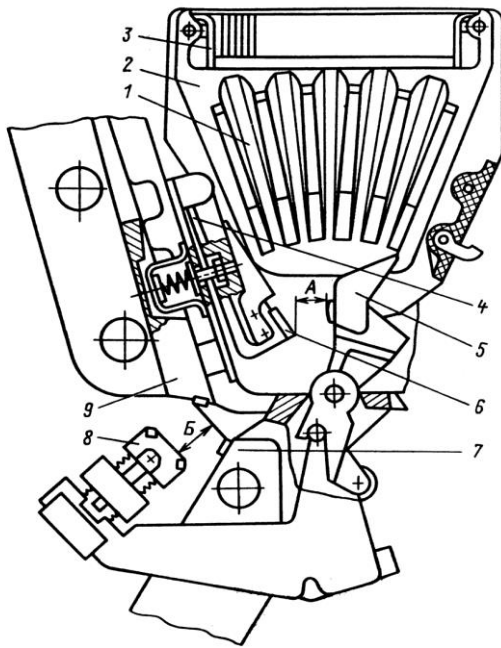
Контактна група і дугогасильний пристрій автоматичного вимикача серії «Електрон»: 1-сталі пластини; 2-дугогасильна камера; 3 - пластмасова кришка; 4 - рухливий контакт; 5 - нерухомий контакт; 6 - рукоятка управління
